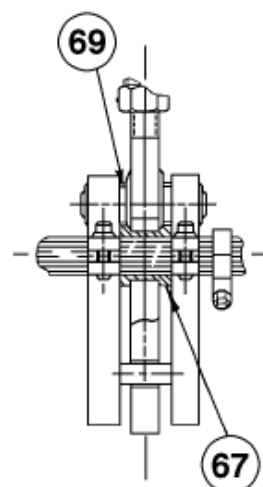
Деталировочный чертеж рычага маховика. Приводы размера В и С
